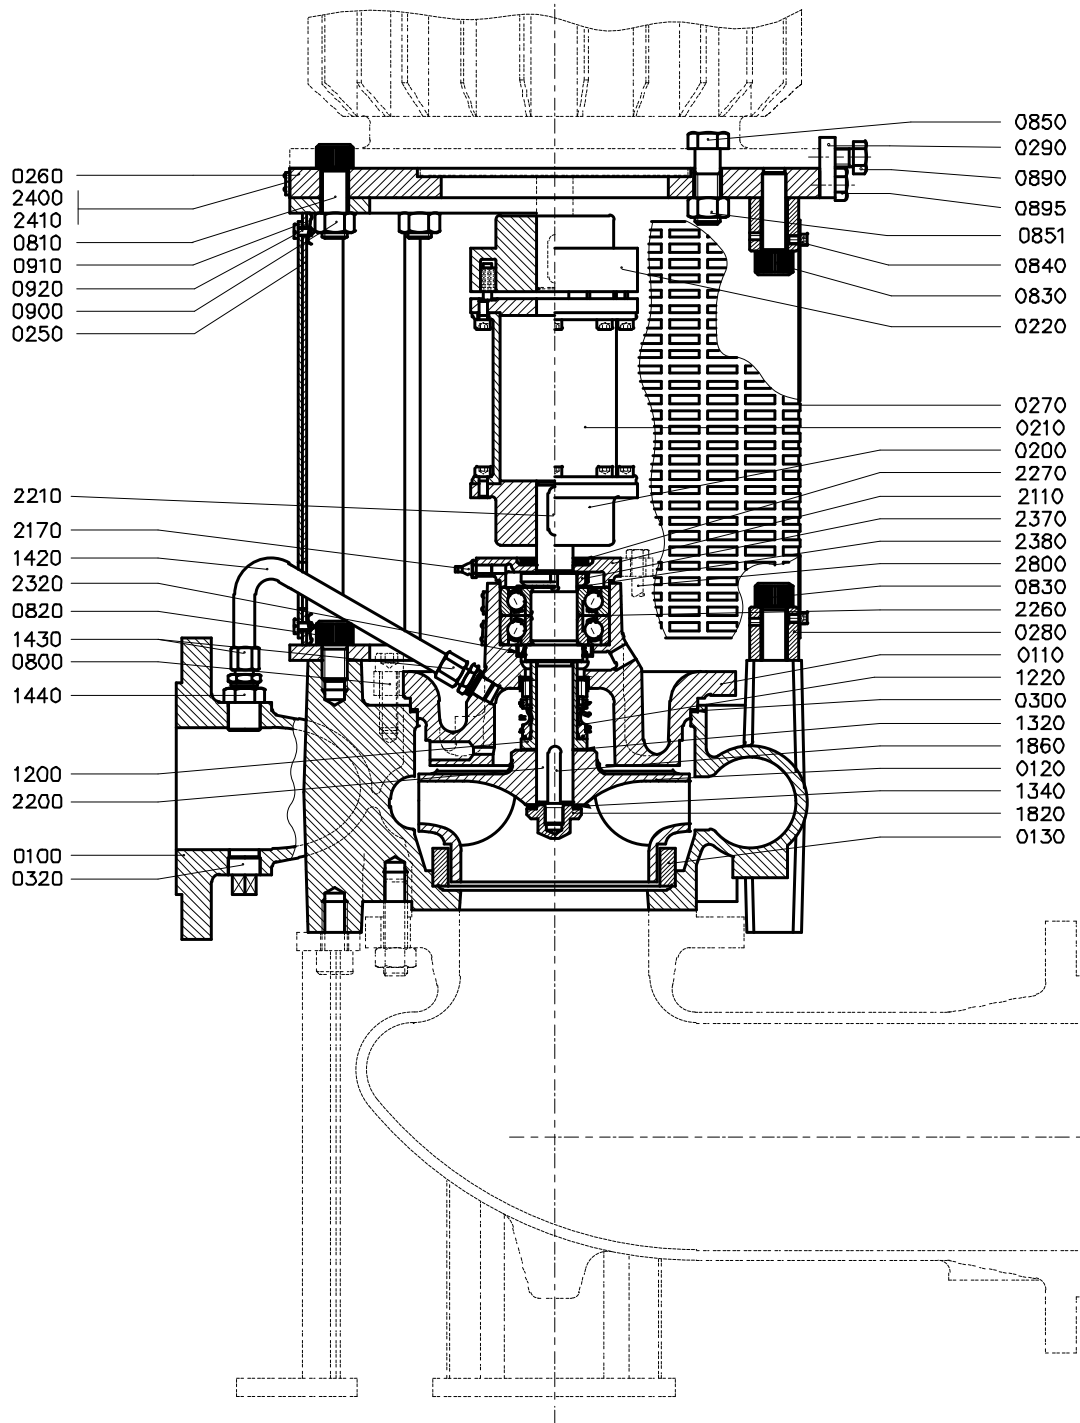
Чертеж в разрезе ..-315/..-400.
